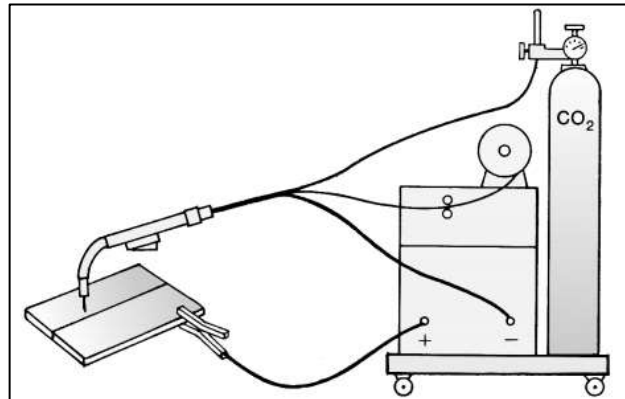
Esquema básico de un equipo de soldadura MIG
